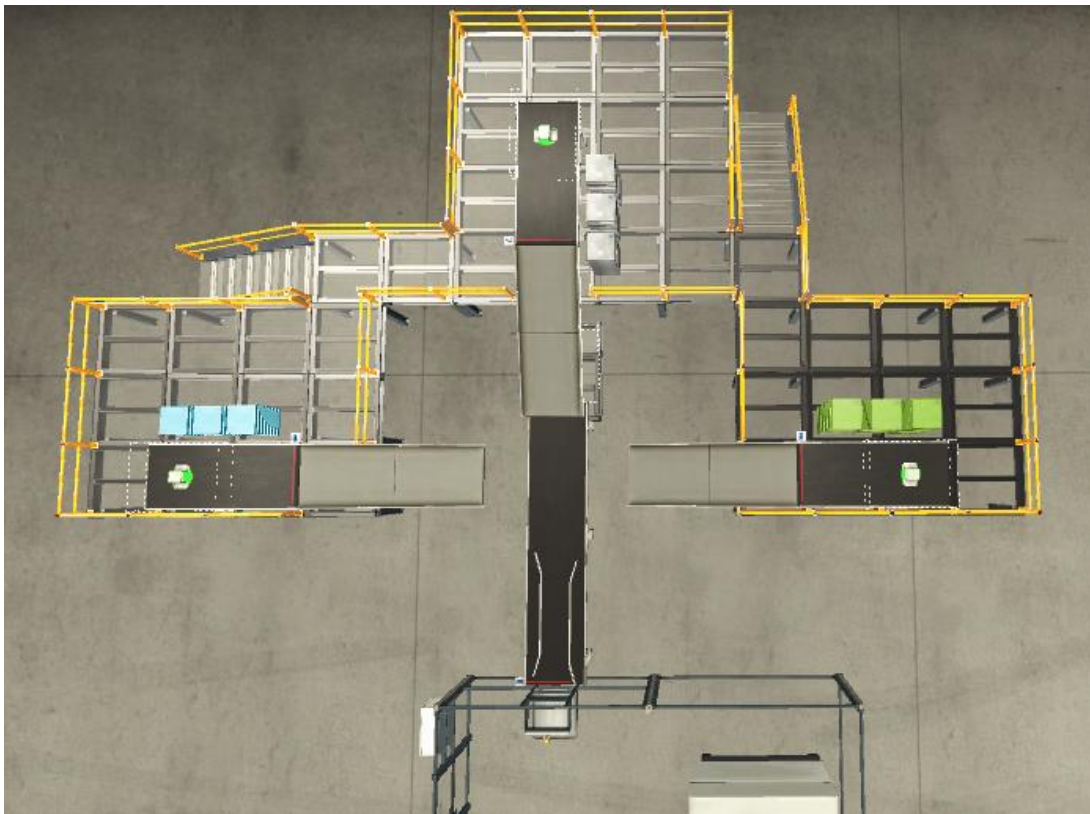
Vista en planta del sistema suministrador de piezas para CNC bases.
